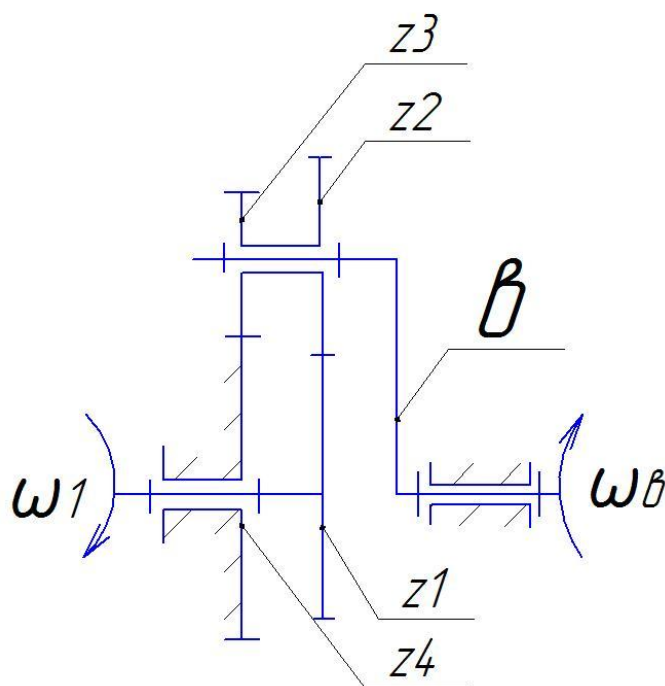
Структурная схема двухрядного планетарного редуктора с двумя внешними зацеплениями
